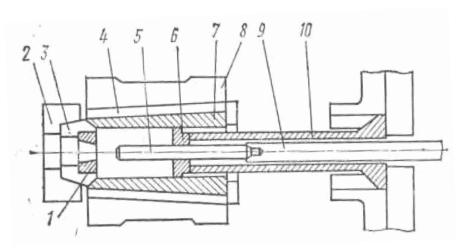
Конструктивная схема штампового инструмента для выдавливания труб на горизонтальном гидравлическом прессе: 1 — матрица; 2 — кольцо промежуточное; 3 — кольцо матрицедержателя; 4 — промежуточная втулка; 5 — игла; 6 — пресс-шайба; 7 — внутренняя (рабочая) втулка; 8 — контейнер; 9 — иглодержатель; 10 — шплинтон
